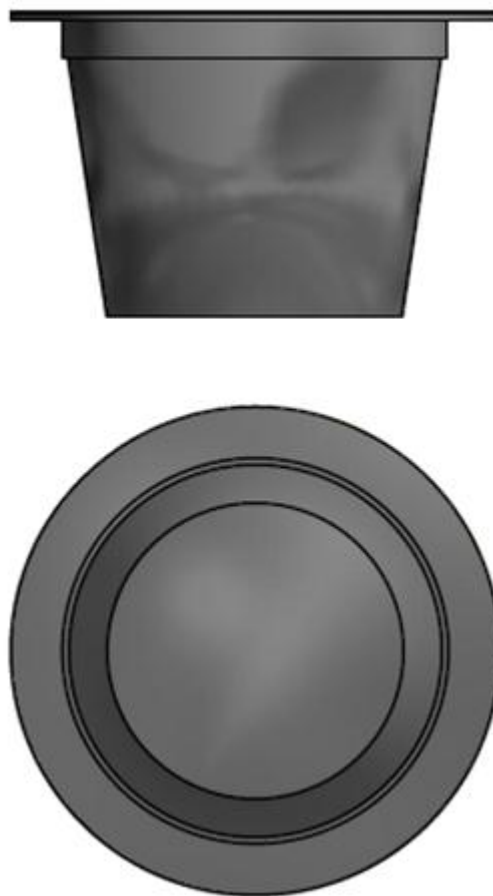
Alzado y planta de la cápsula Ne-Cap. [NEC12]
